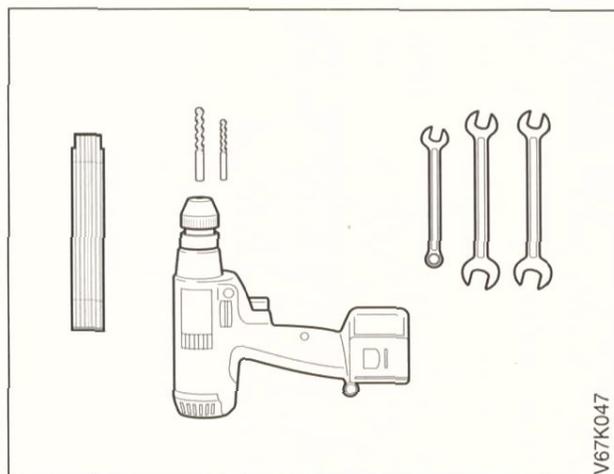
Werkzeug für Montage: Zollstock, Bohrmaschine, 8,5mm-Metallbohrer, 12mm-Steinbohrer, 13er Maulschlüssel und 2 Maulschlüssel (Größe: 21 und 24 mm)
